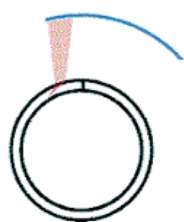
Schweißnahtprüfung am Rohr mit Array-Technik
